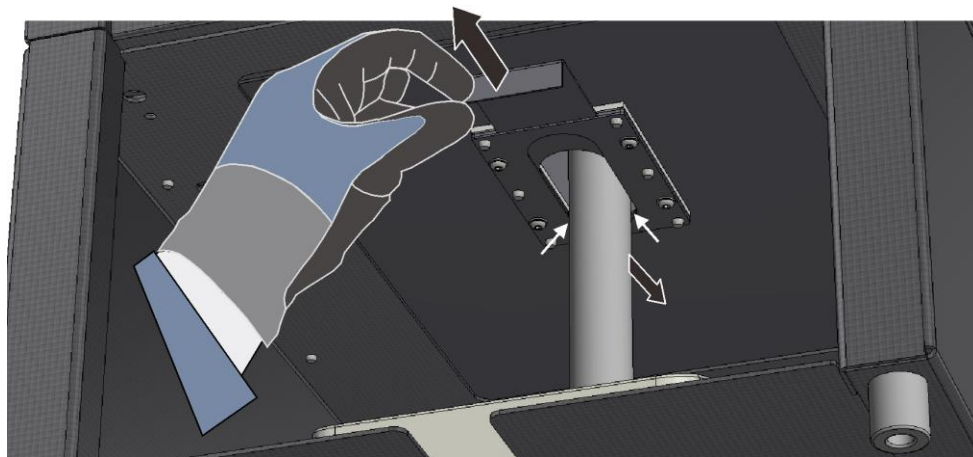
Abrir o dispositivo deslizante para vedar (semelhante à figura)
